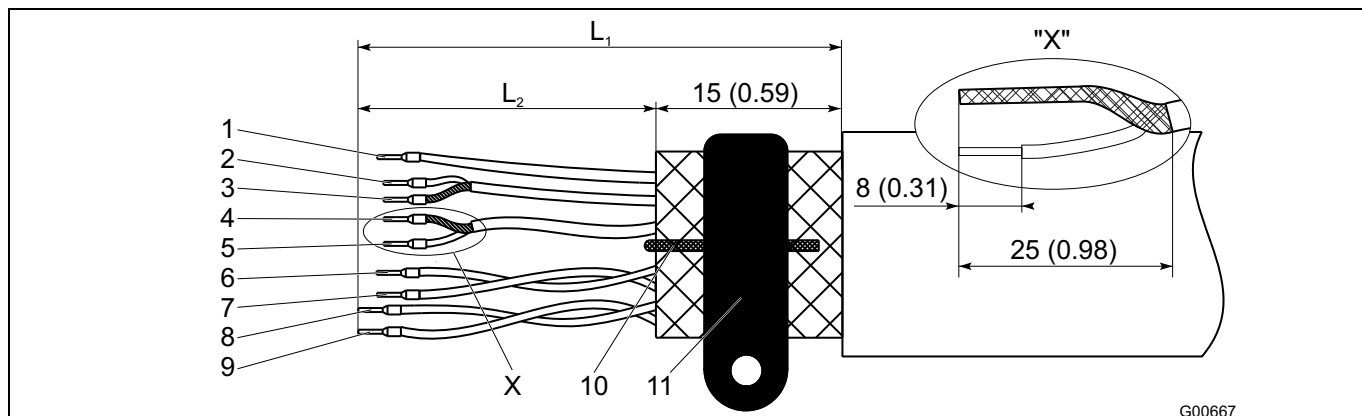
Lado do transdutor de medição, dimensões em mm (inch)
